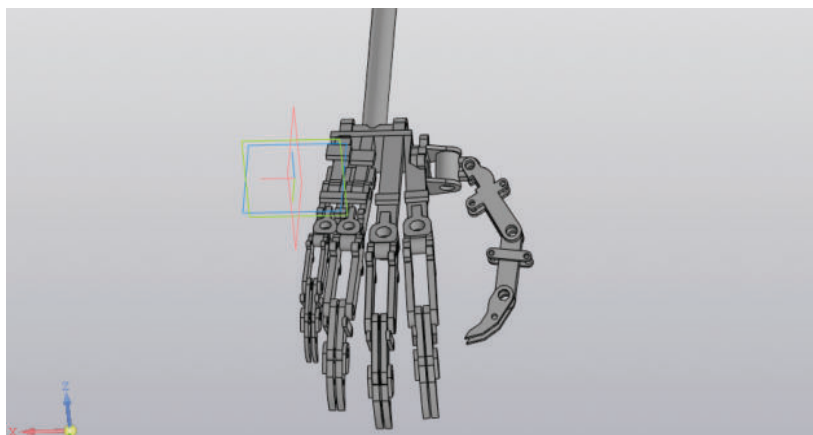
3D-модель конструкторской разработки (вид сверху)
